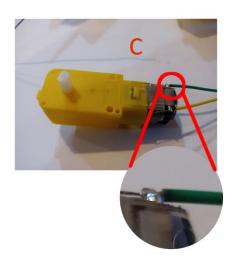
Estañado y soldado de los cables en los motores.
